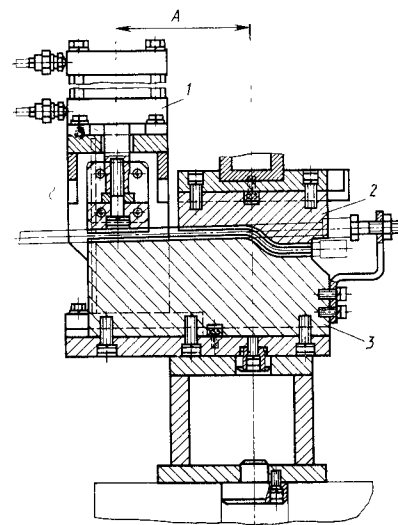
Штамп для гибки трубы с применением пневмоцилиндра для зажима заготовки
